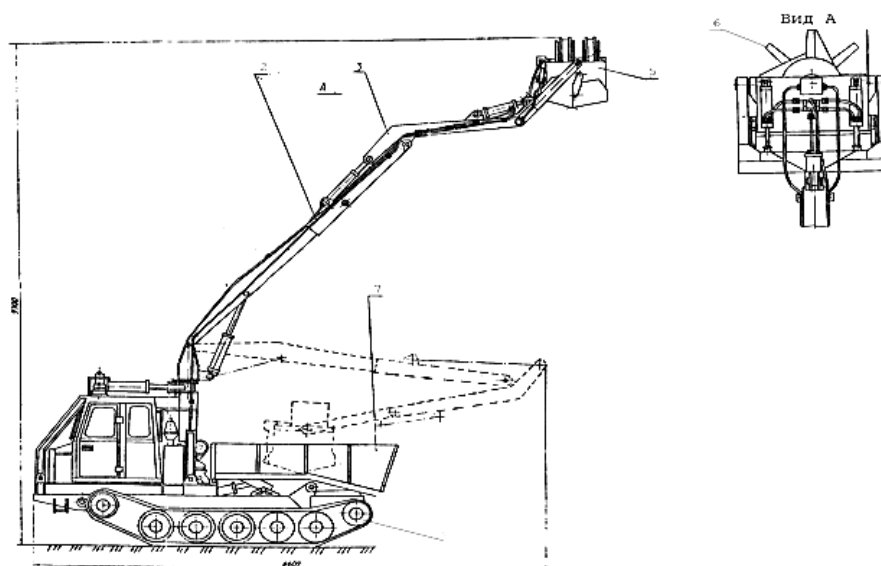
Самоходная установка для заготовки древесной зелени.
